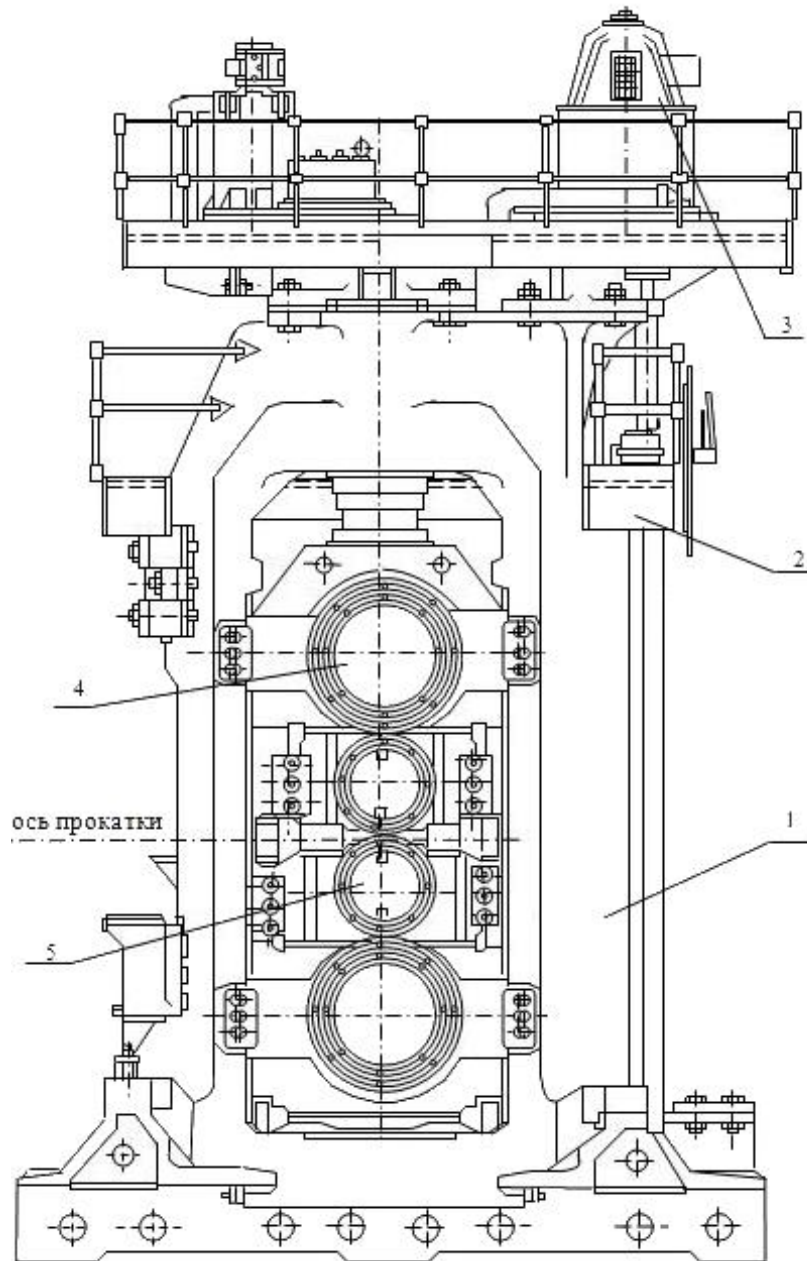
Чорнова кліть «кварто»: 1 – станина; 2 – шпинделі; 3 – електродвигун; 4 – валок опорний; 5 – валок робочий.
